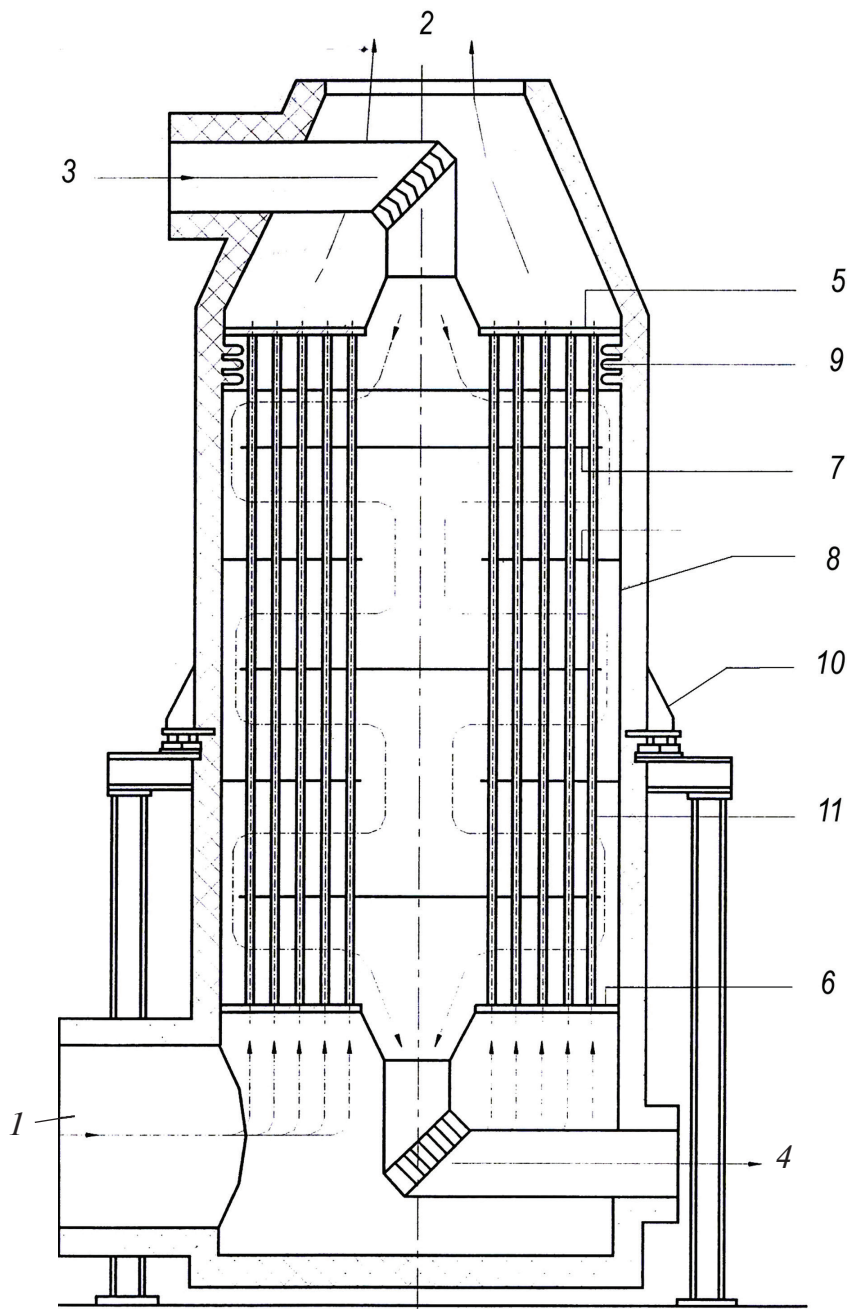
Схема трубчатого регенератора GEA [12]:
